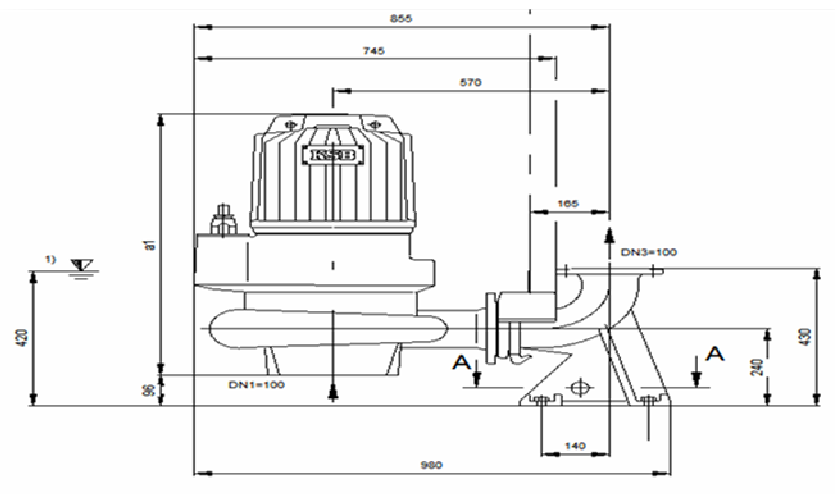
Les dimensions de la pompe choisie (vue en profil)
